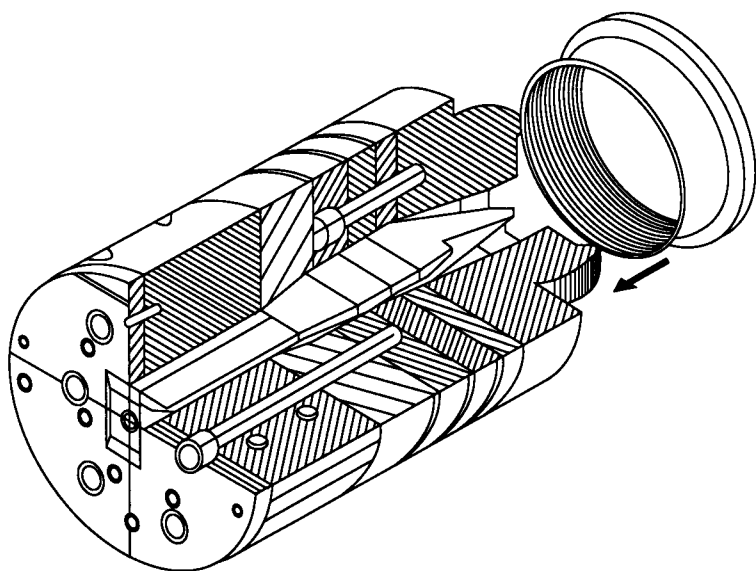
Экструзионная головка с наворачивающейся резьбовой втулкой для фланцевого крепления головки [4]
